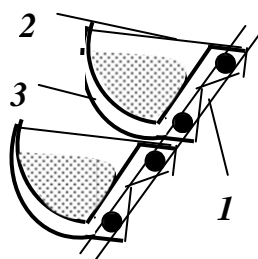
Схема ковшової стрічки зневоднювального елеватора:
